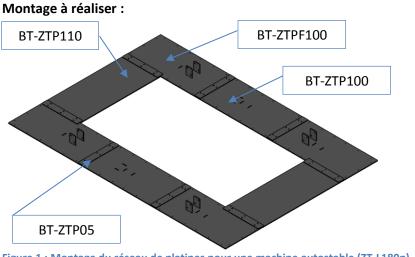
Montage du réseau de platines pour une machine autostable (ZT-L180p)
